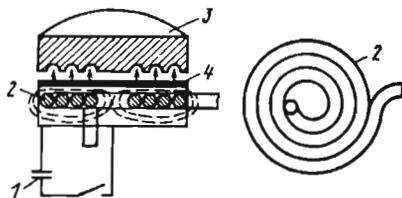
Схема установки для магнитоимпульсной штамповки из плоских заготовок
